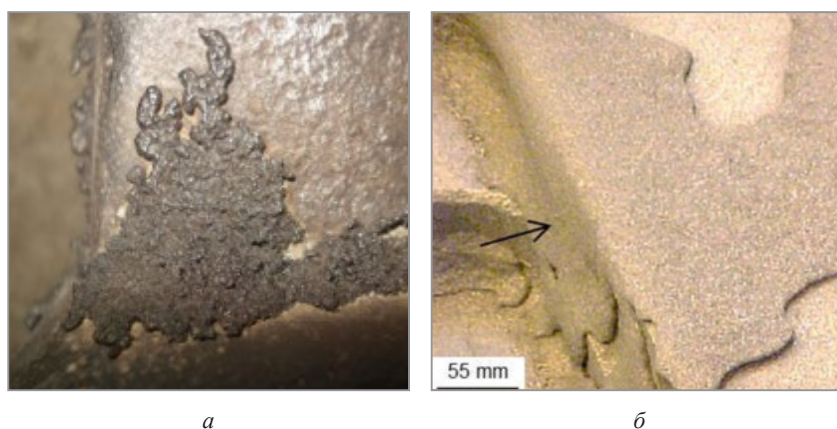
Механический (металлизированный) пригар на поверхности отливок
